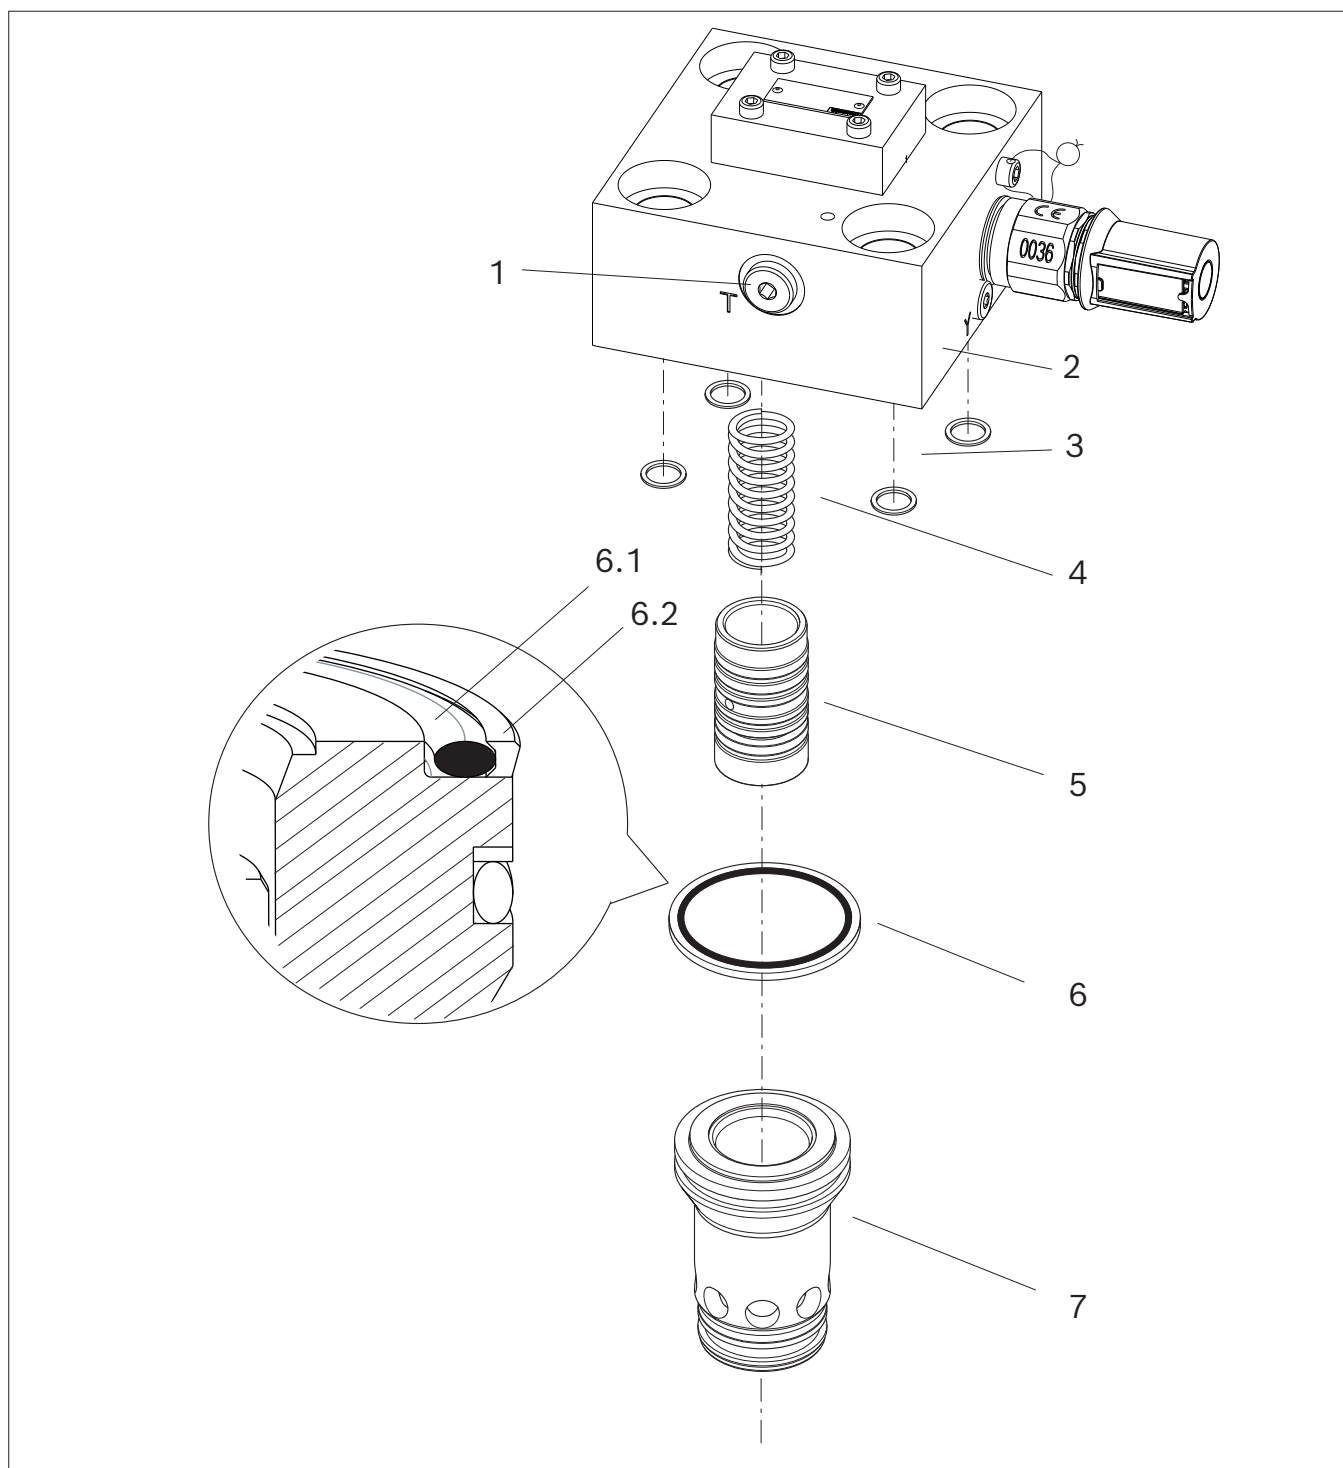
Vue éclatée LFA40DBW2-7X/...E
